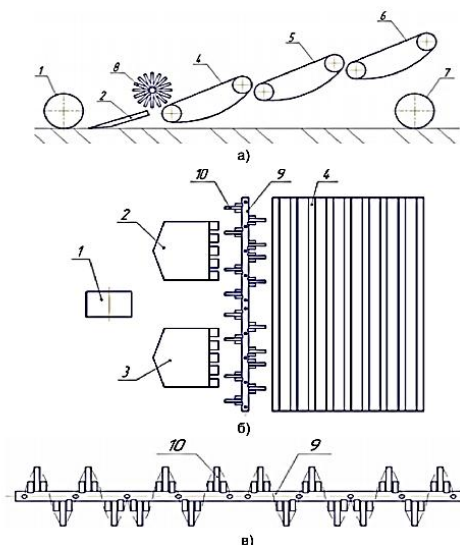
Схема копача: а – копач (вид збоку); б – копач (вид зверху); в – розрихлювач пласта; 1 – опорне колесо; 2, 3 – лемеші; 4 – швидкісний елеватор; 5 –
